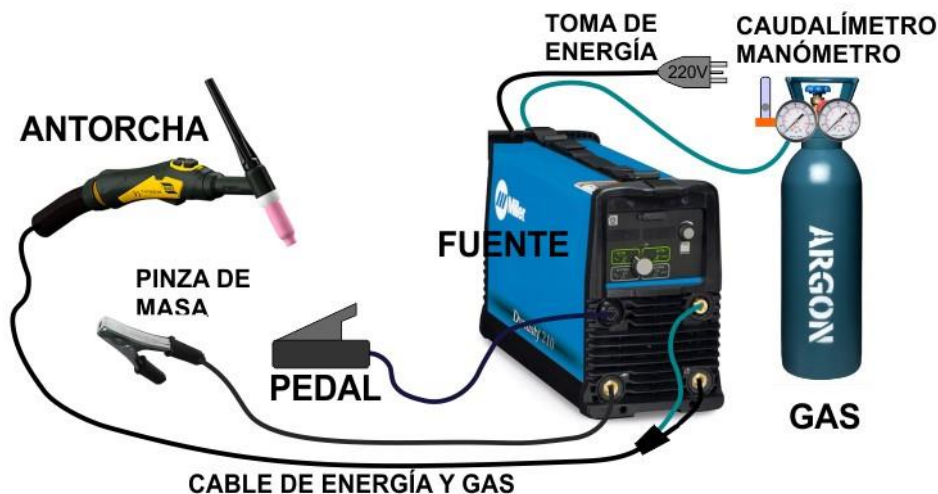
Equipo de soldadura TIG (fuente: herreros argentinos) [13]
